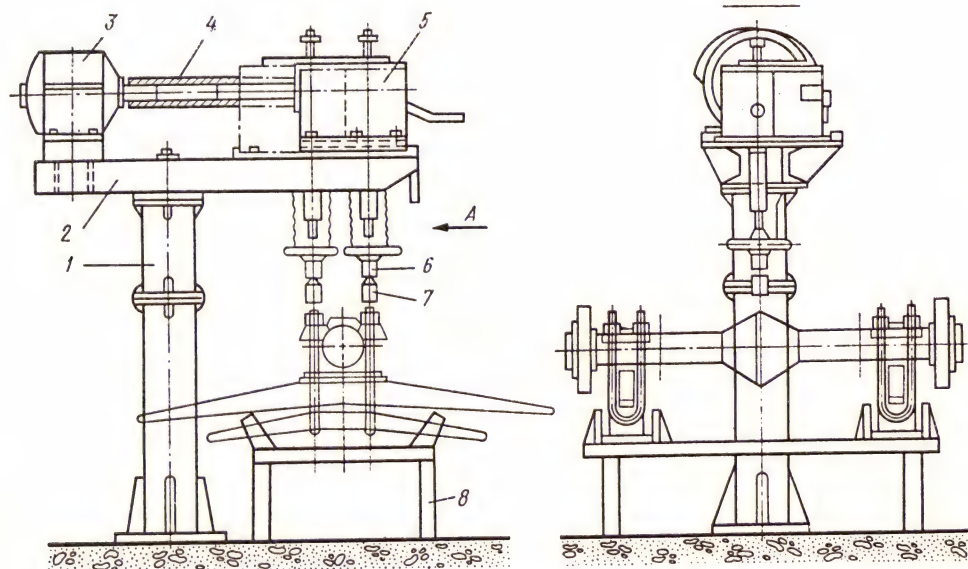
Стенд для отвертывания гаек стремянок рессор грузовых автомобилей:
